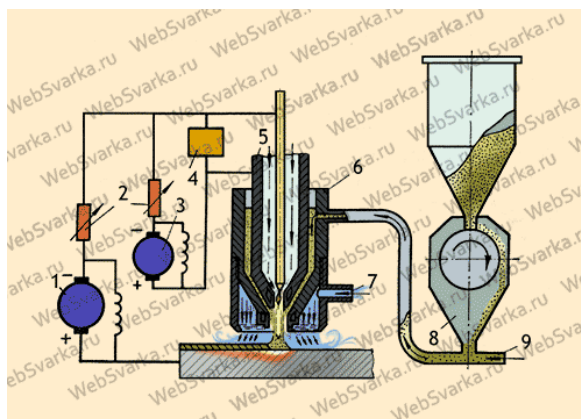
Наплавка с подачей порошка в сварочную ванну струёй защитного газа: 1, 3 – источники питания; 2, 4 – балластные сопротивления; 5, 6 – боковые стенки устройства; 7 – подача защитного газа; 8 – бункер для порошка с регулятором подачи; 9 – транспортирующий газ. Следование этой схеме позволит учителю познакомить учащихся с основами газопорошковой наплавки, подготовив их тем самым к дальнейшему углублённому профессиональному обучению.
